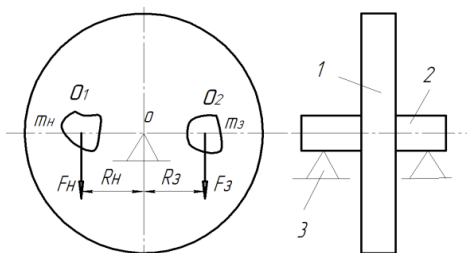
Схема зрівноваження деталей під час статичного балансування: 1 – деталь; 2 – оправка; 3 – опора
